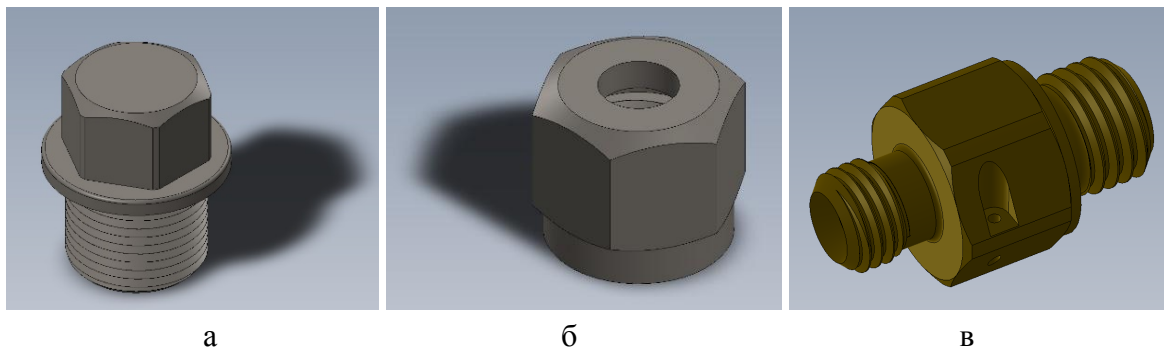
Приклади деталей: а – накривка; б – гайка накидна; в – штуцер
